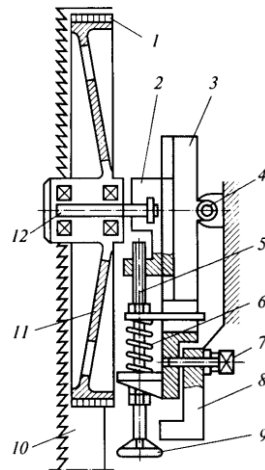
Верхній пильний шків стрічкопилкового верстата: 1 – бандаж; 2 – повзун; 3 – кронштейн; 4, 12 – осі; 5 – гвинт; 6 – пружина; 7 – регулювальний гвинт; 8 – станина; 9 – маховичок; 10 – пилка; 11 – шків
